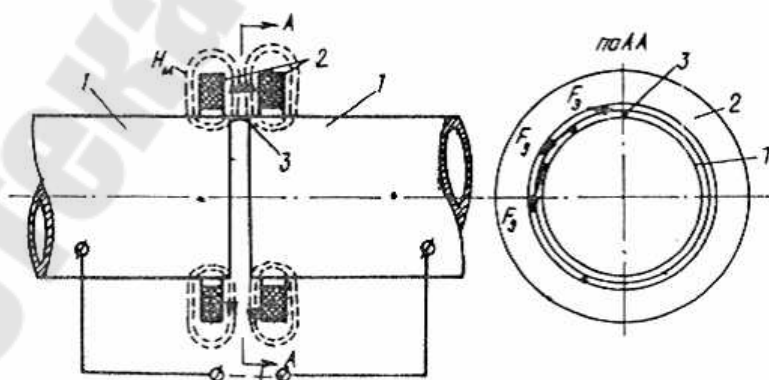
Схема сварки вращающейся магнитоуправляемой дугой: 1 - свариваемые трубы; 2 - кольцевые магниты; 3 - столб сварочной дуги; H_m - направление магнитного поля в зазоре; F_l - сила Лоренца или направление перемещения дуги
